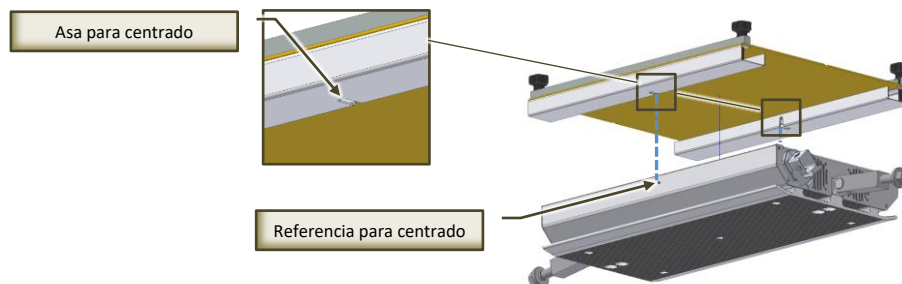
Posicionamiento placa de unión en placa inferior prensa
